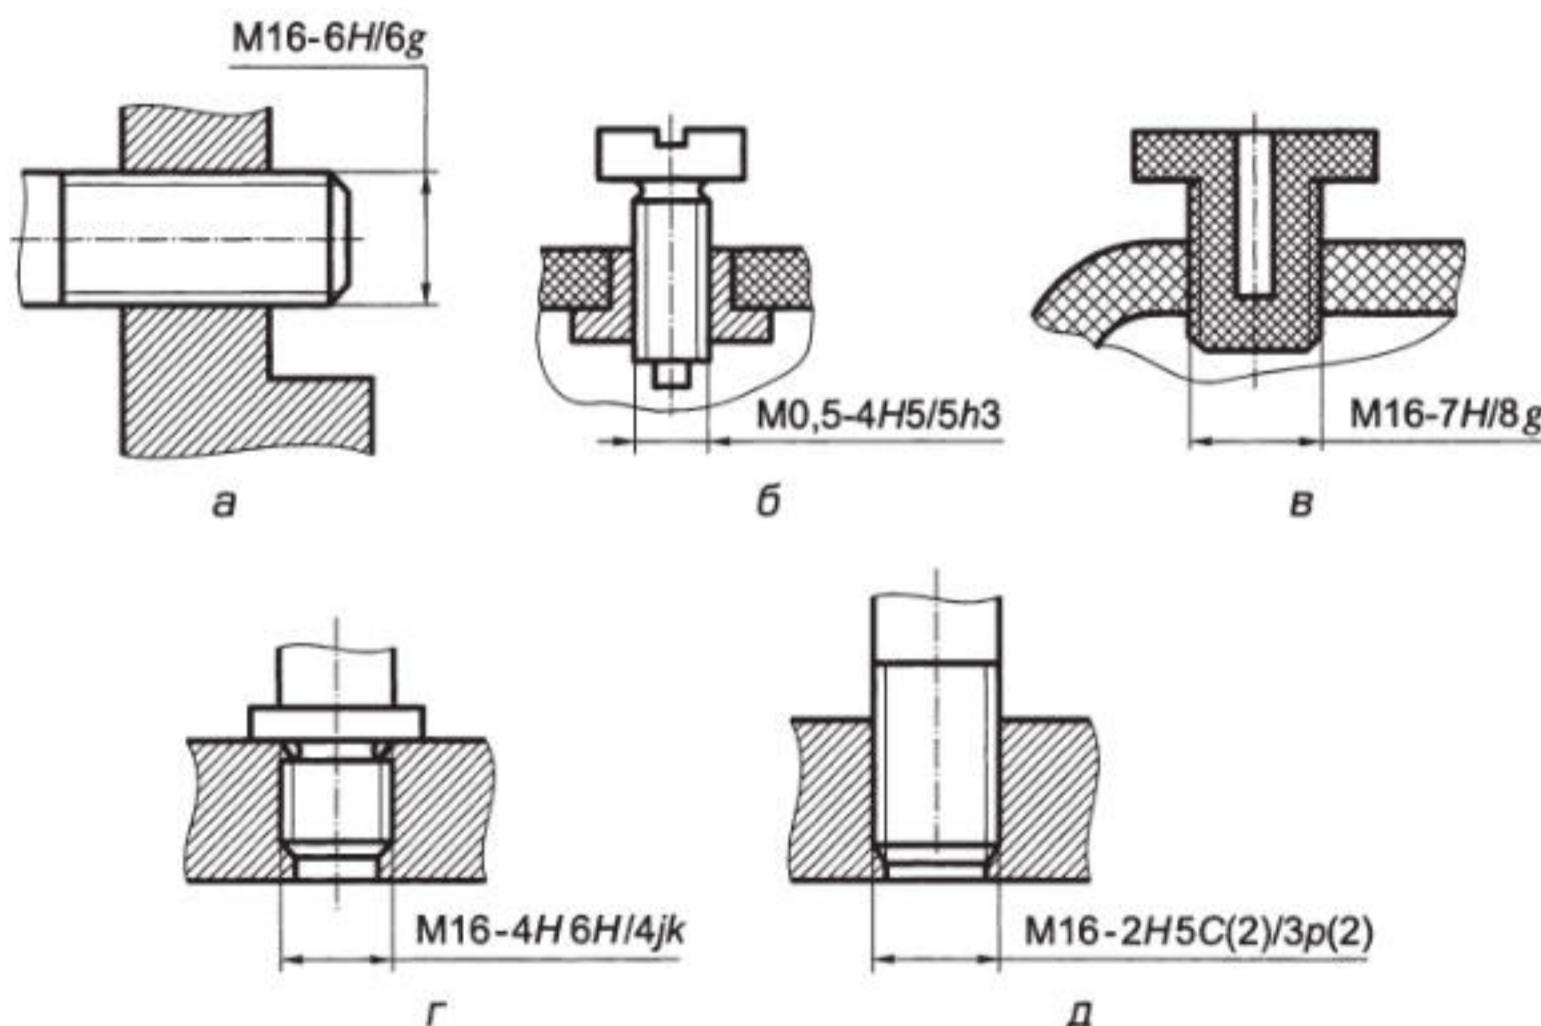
Условные обозначения посадок в резьбовых соединениях с метрической цилиндрической резьбой:
